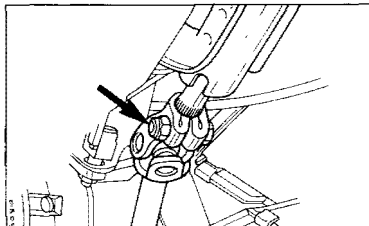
Болт зажима вилки шарнира, соединяющего промежуточный вал с валом рулевой колонки
